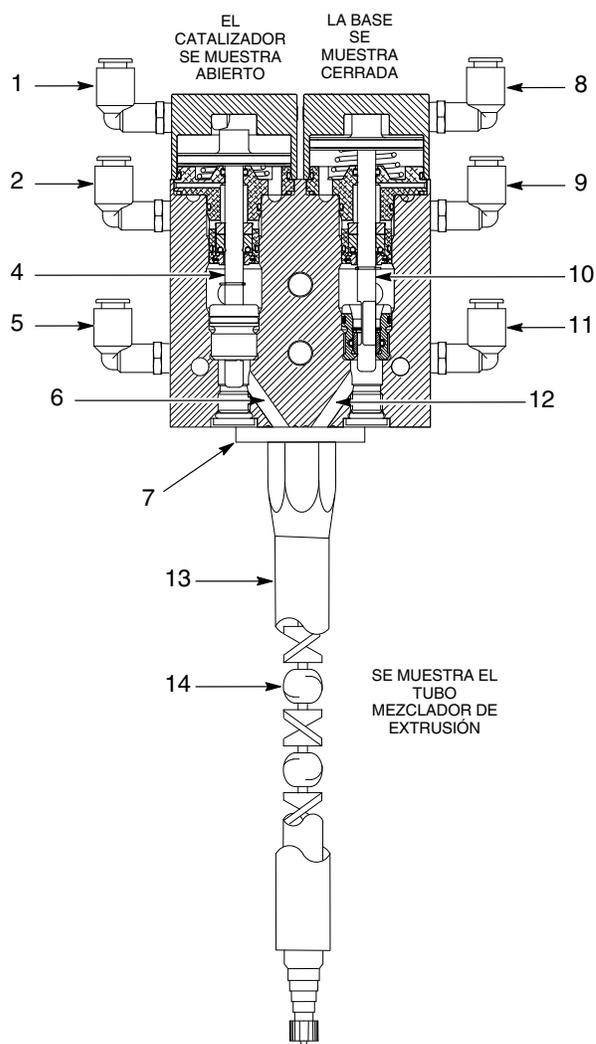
Vista en corte de la válvula de aplicación de dos componentes (Se muestra montaje en distribuidor)
